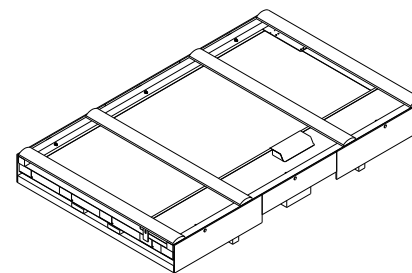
Вариант 1 - упаковка, допускающая механизированную погрузку дверного блока (упаковочная пленка не показана)
